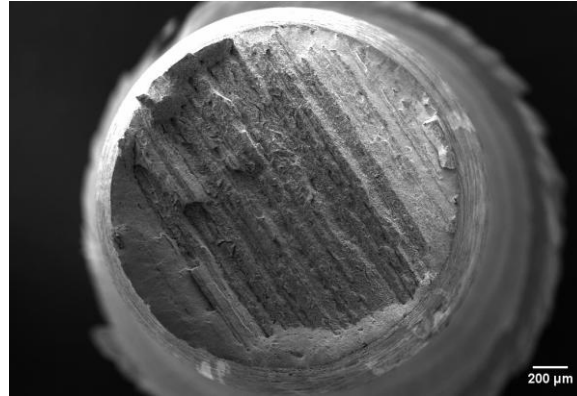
Superficie de fractura en un ensayo de tracción según la dirección transversal de las barras
